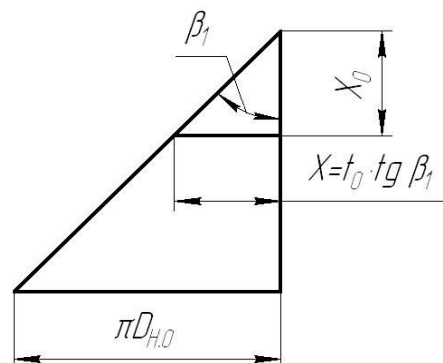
Развертка витка нарезки косозубой шестерни $z = 64$
